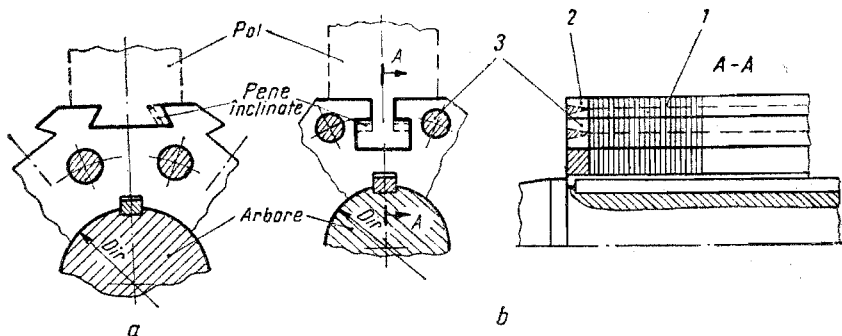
Butuc rotor pentru mașina sincronă :
